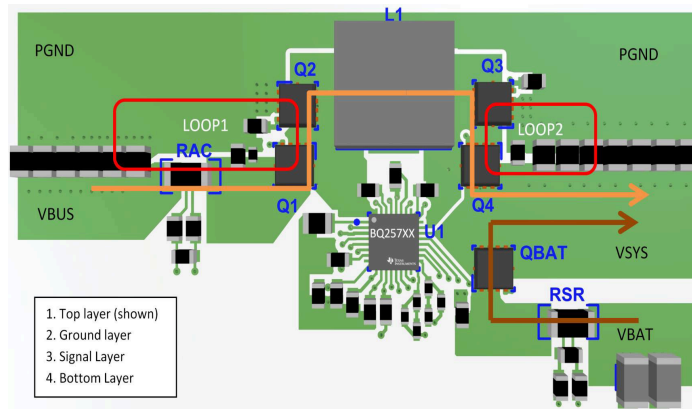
PCB 堆叠和顶层元件放置的布局示例
